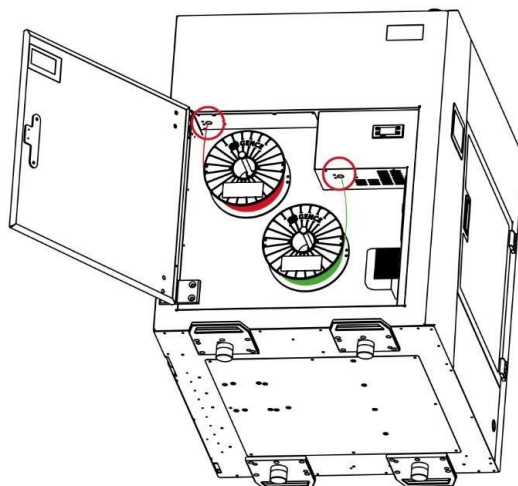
Правильная загрузка материала для Tool 0 (термоголовки 0) и Tool 1 (термоголовки 1)
